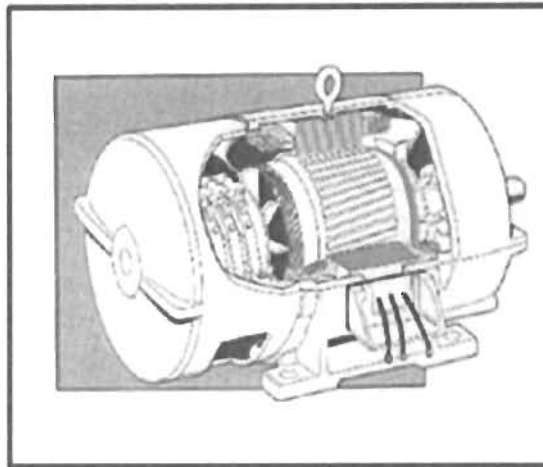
Machine asynchrone à rotor bobiné [1]
